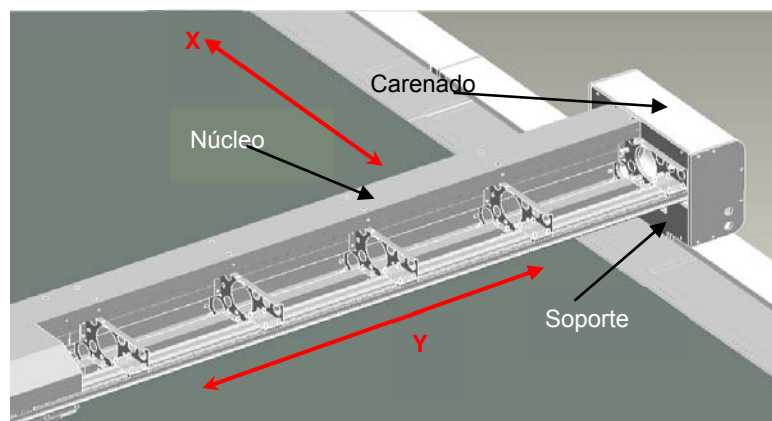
Estructura del puente original (cortesía Roglan Equipment)
